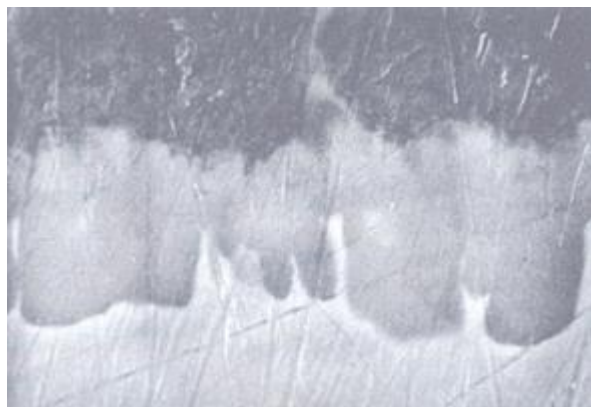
Pozinkovaný a nepozinkovaný závit šroubu vystavený korozi [5]
